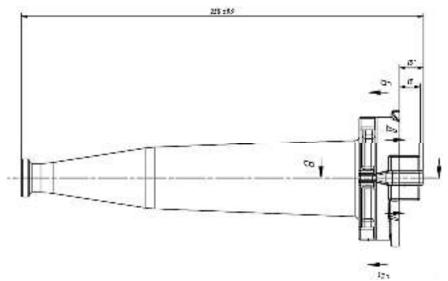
Конструкция ручного пожарного ствола РС-50А.
